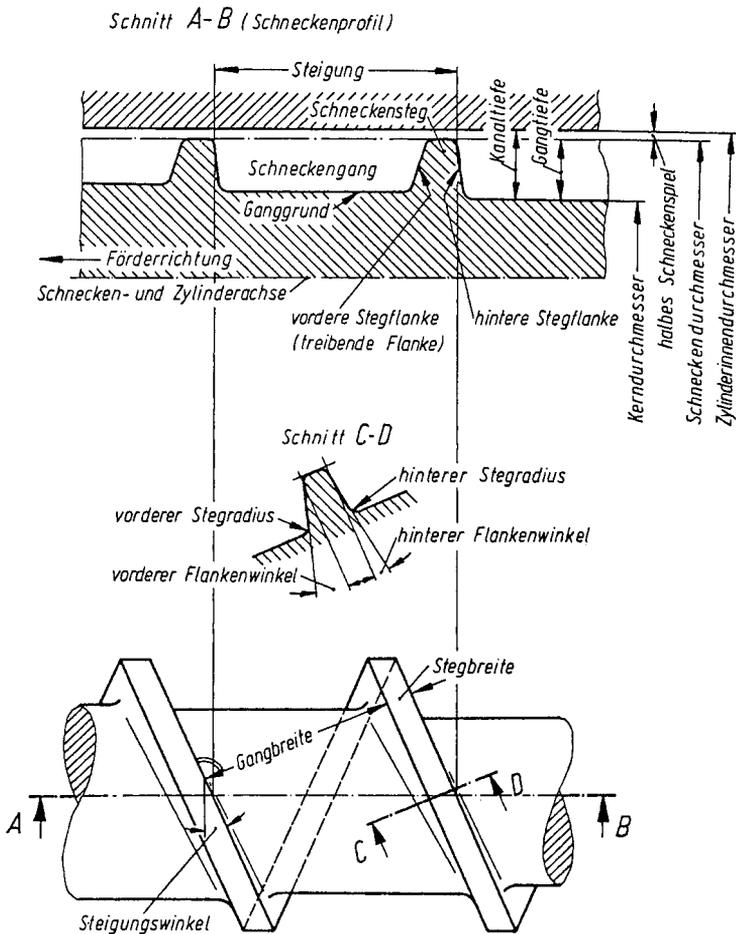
Begriffe zur Schneckenengeometrie (DIN 24450)
